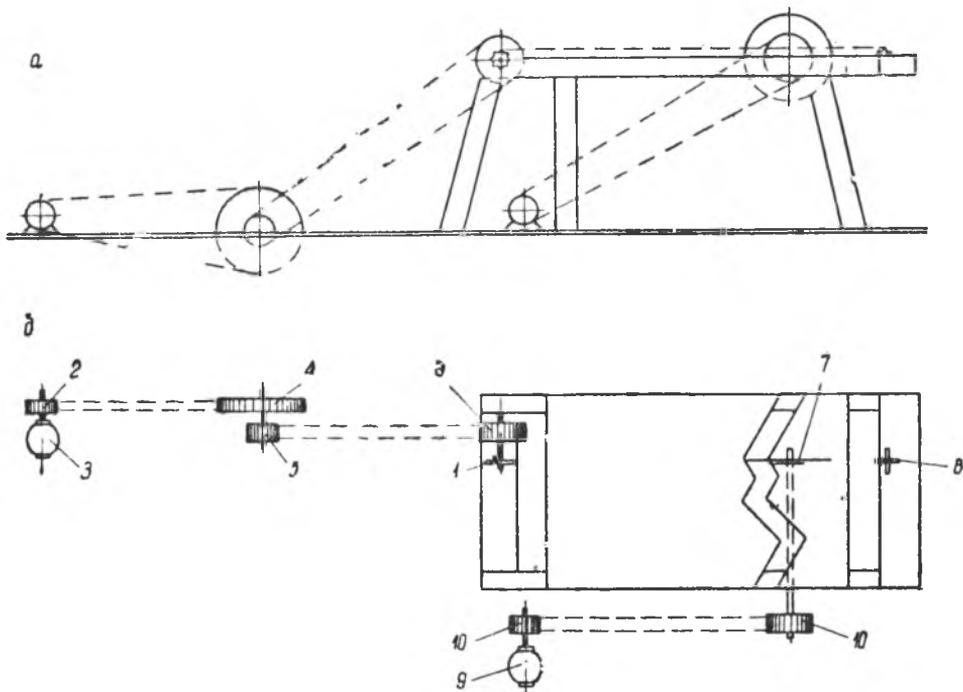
Схема установки гонторезного станка с приводами пилы и цепи Галля:
